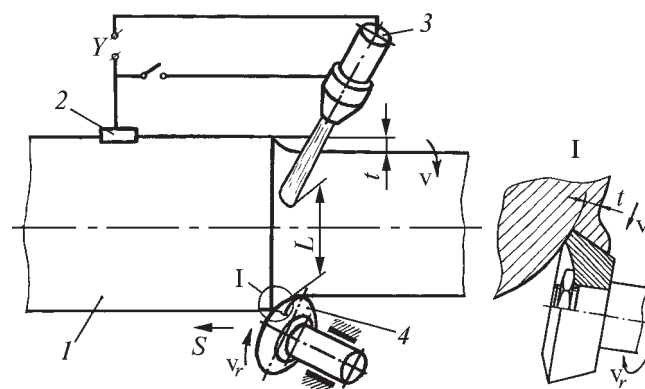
Обработка ротационным резцом с предварительным плазменным нагревом (v – скорость главного движения; v_r – скорость дополнительного движения; S – подача; t – глубина резания; L – расстояние от пятна нагрева до инструмента; I – сила тока плазменной дуги);
